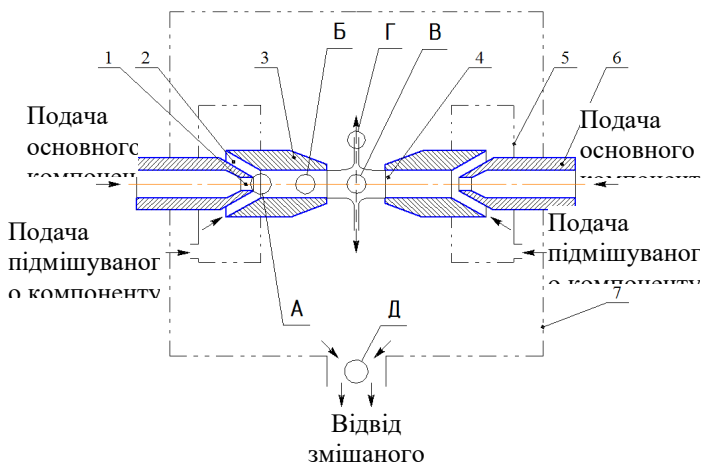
Схема протитечійно-струминного змішувача: 1 – робоче сопло; 2 – приймальна камера; 3 – камера змішування; 4 – сопло камери змішування; 5 – камера подачі підмішуваного компонента; 6 – робочий патрубок; 7 – камера збору рідини. А, Б, В, Г, Д – зони змішування
